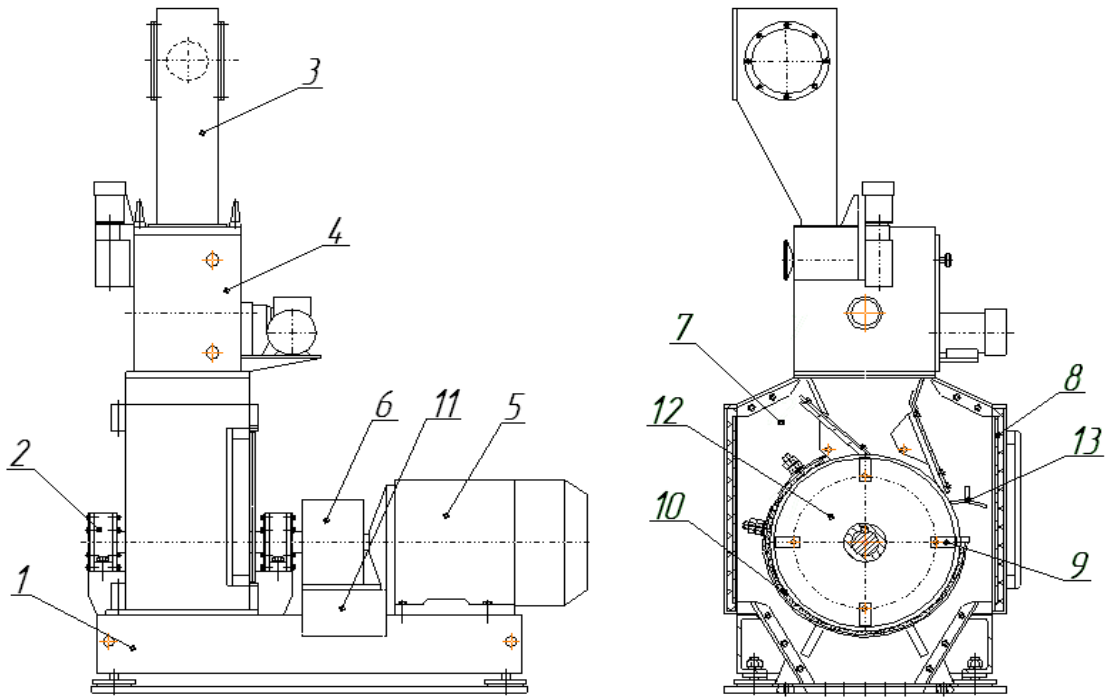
Загальний вигляд дробарки А1-ДМ2Р:
